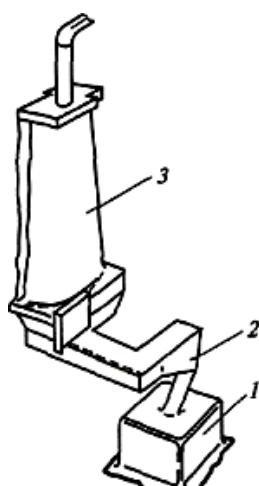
Внешний вид плавильно-заливочной установки УПВ6-НК
